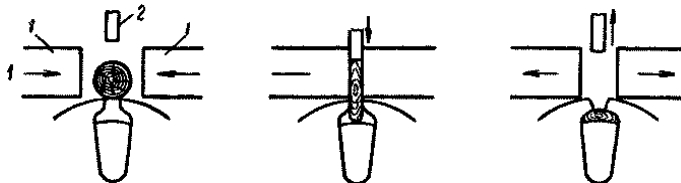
Схема работы станка для крепления обмотки в пазу.
